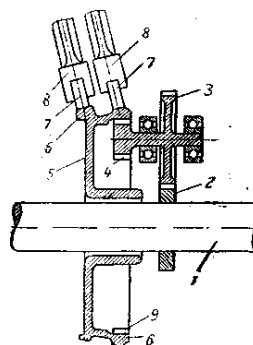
Схема газораспределительного устройства двухрядного звездообразного
